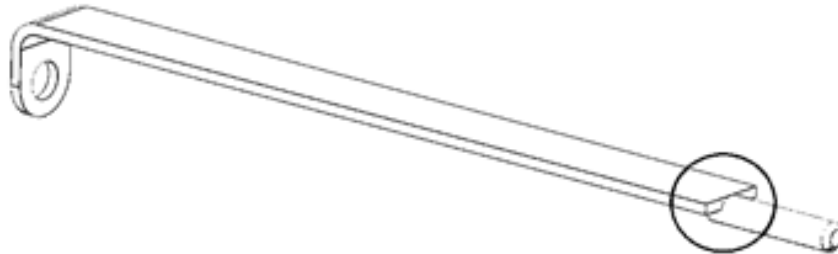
Конструктивне виконання елемента зварного з'єднання
